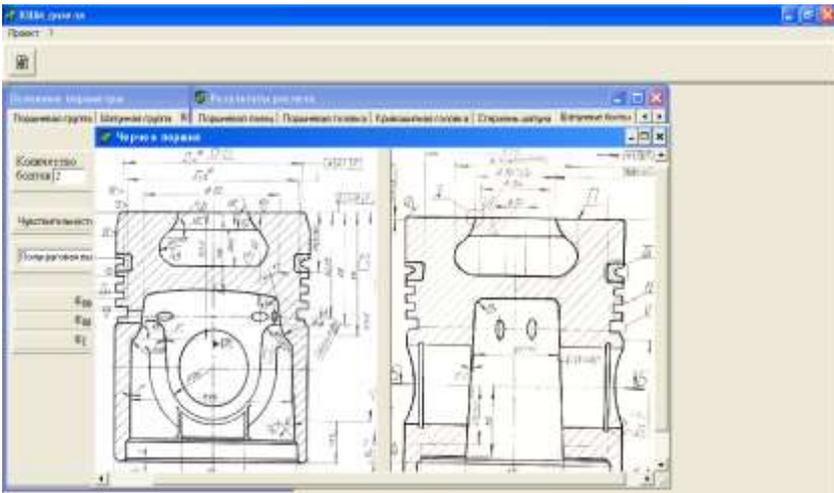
Рабочая документация для изготовления опытного образца поршня
